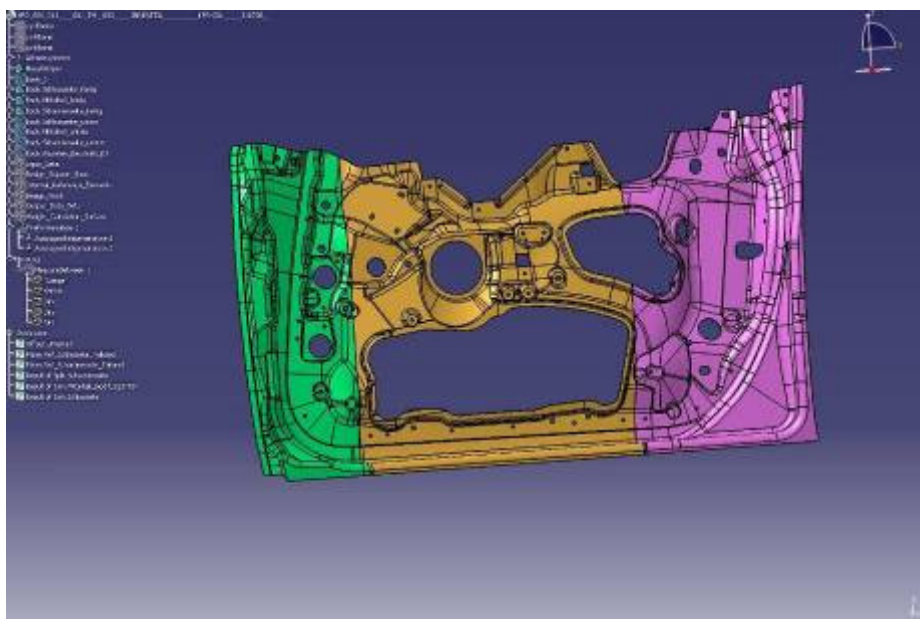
Tür-Innenteil (mit geplanter Schweißnahtlage)
